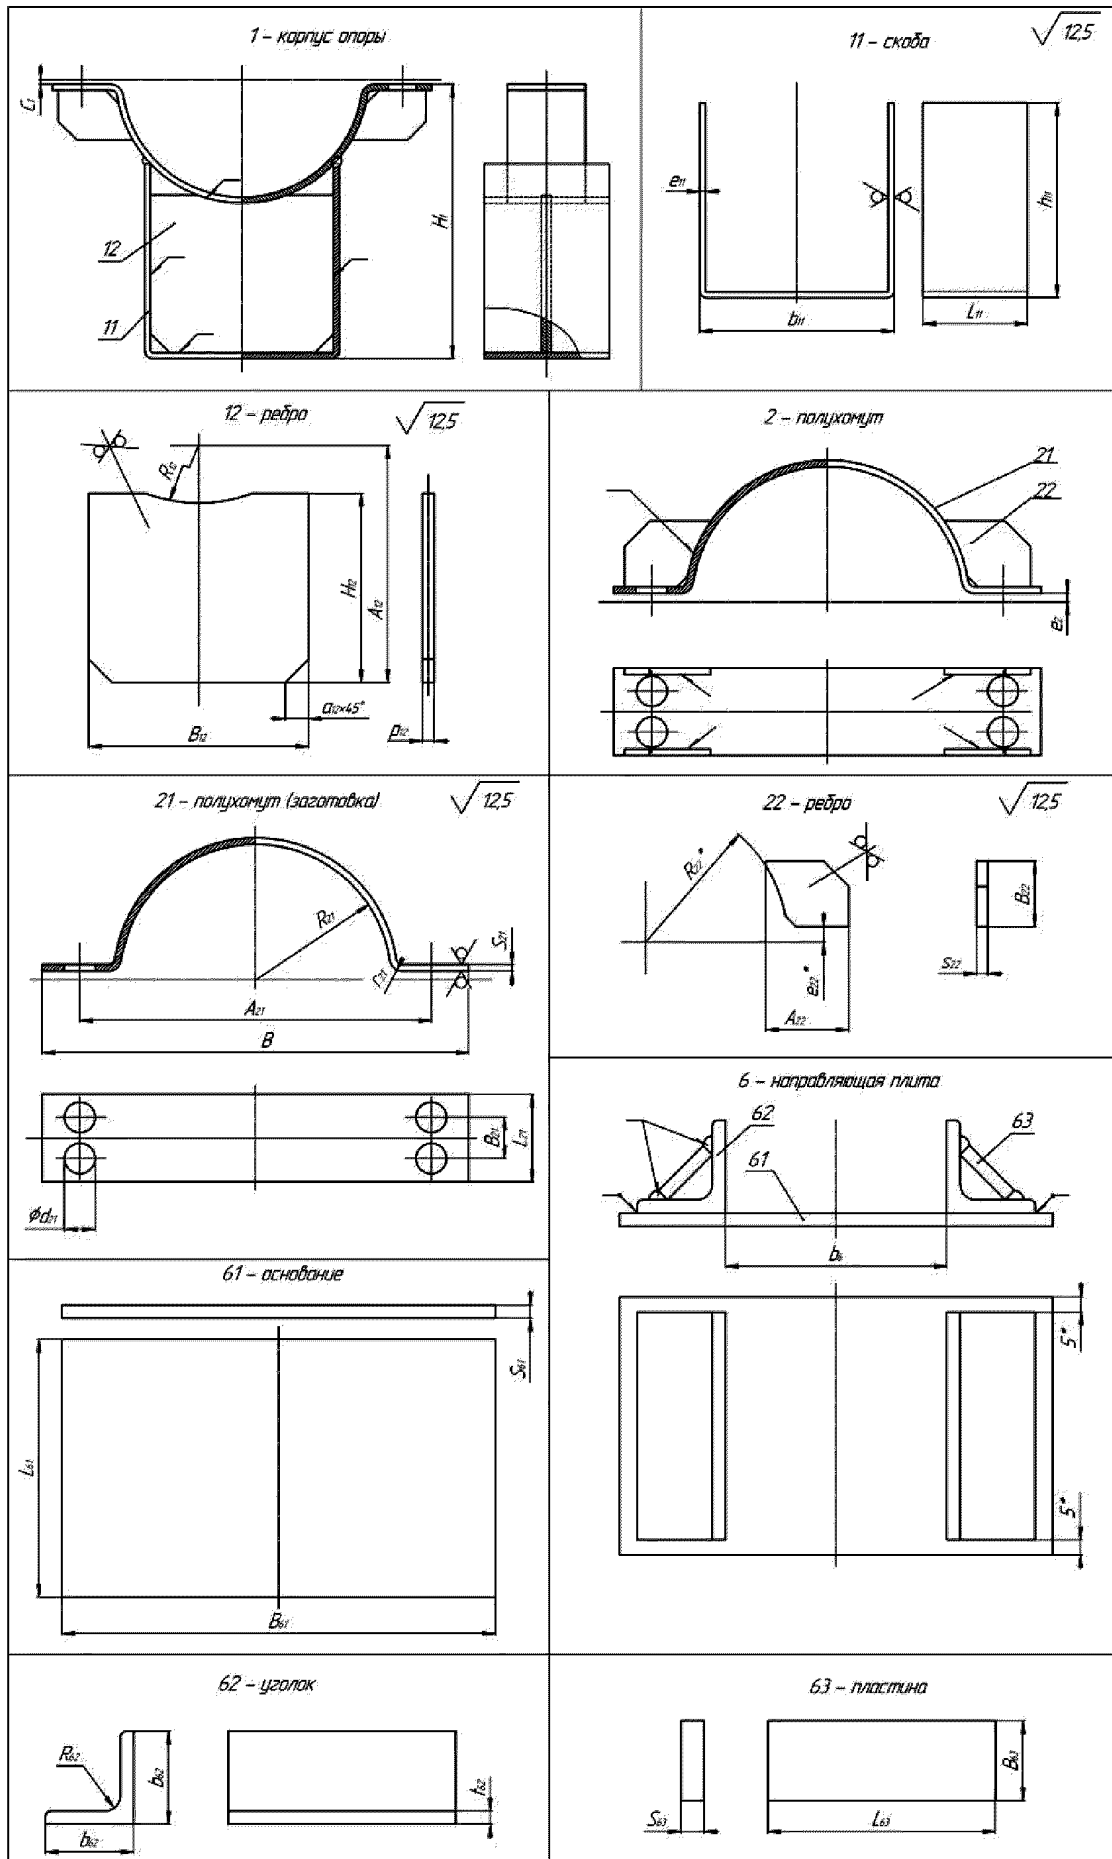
Детали изделий 01-XXXX-G-1C-03-A,
